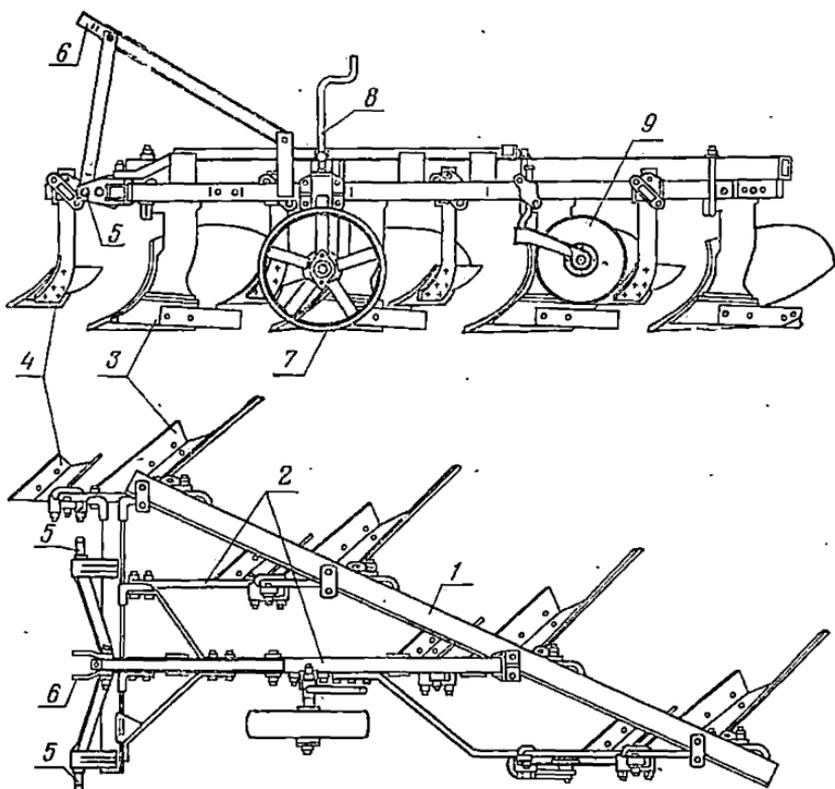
Навесной четырехкорпусный плуг общего назначения:
